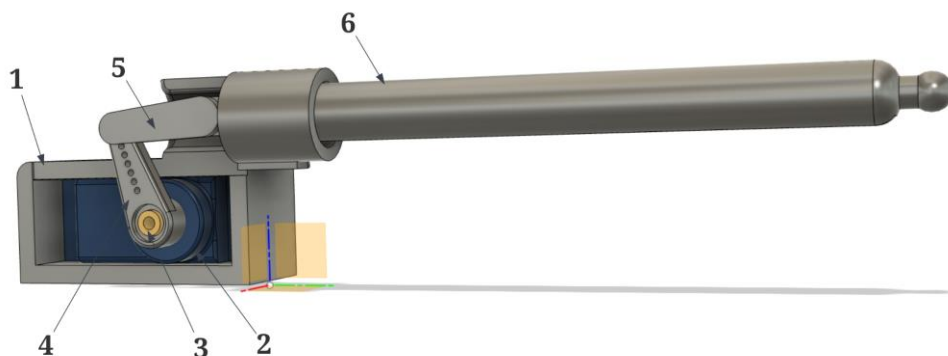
Имитатор гидравлического цилиндра для масштабного макета МШК: 1 – корпус, 2 – сервопривод MG 90, 3 – приводной вал сервопривода, 4 – тяга с креплением на вал сервопривода, 5 – тяга промежуточная, 6 – подвижная опора
